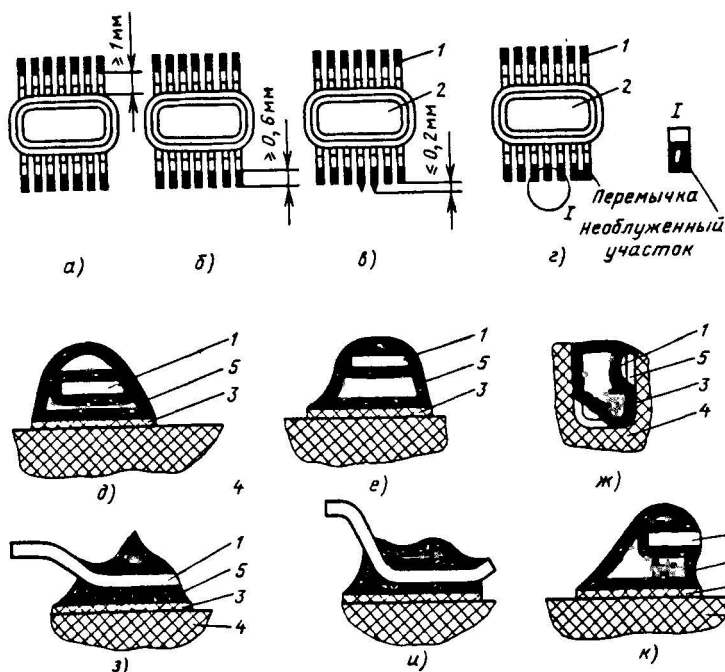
Примеры лужения и пайки выводов планарного корпуса
